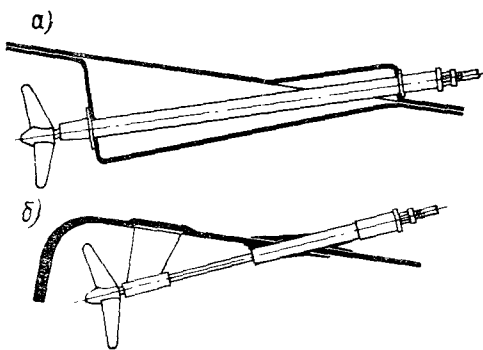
Схема крепления дейдвудной трубы к корпусу.
